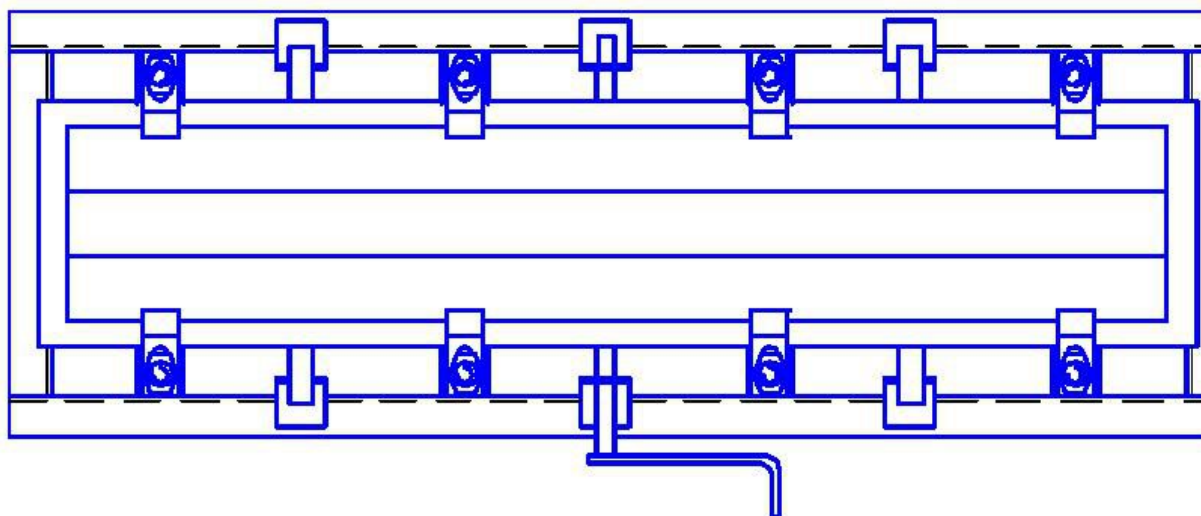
Приспособление для наплавки рабочей поверхности ножа грейдера
